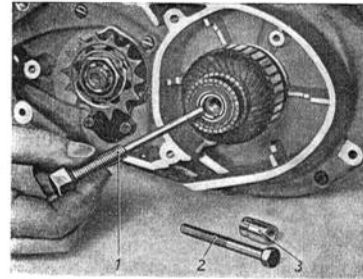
Abziehen des Lichtmaschinenankers mit Abdrückschraube Nr. 0100027 (1). 2 = Ankerbefestigungsschraube, 3 = Unterbrecherrücken
